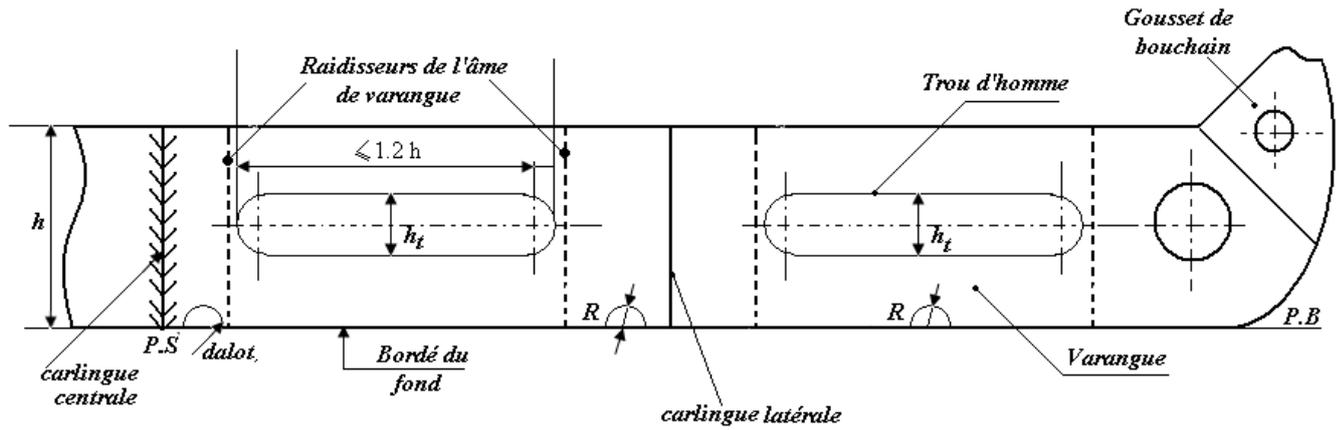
Construction de la varangue évidée avec des trous d'homme horizontal.
